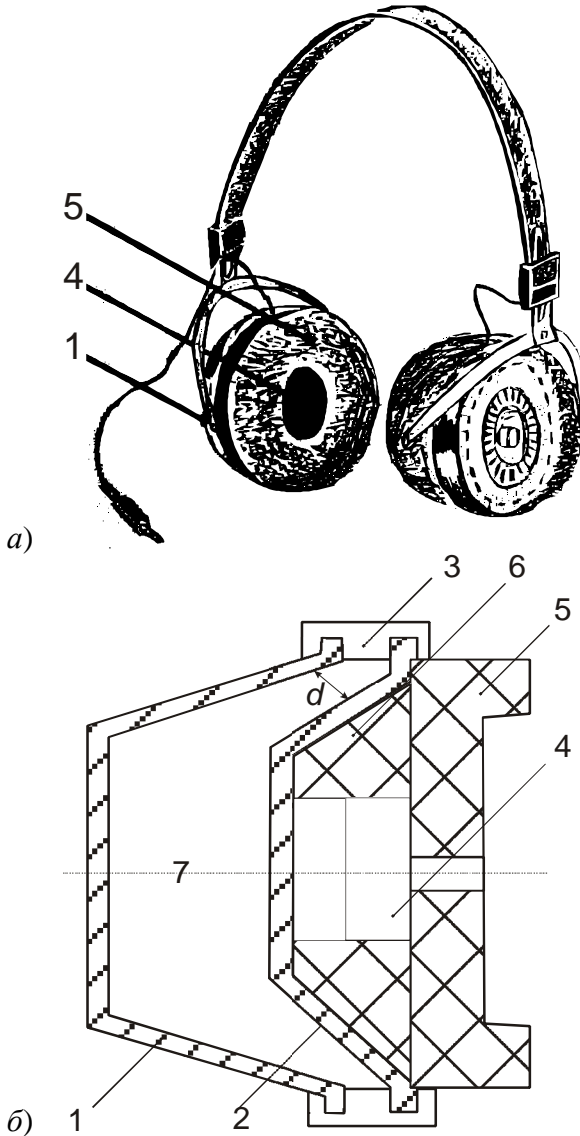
Головний телефон Абракітова [182]: *a* - зовнішній вигляд (дизайн) стереотелефонів; *б* - переріз: 1 - зовнішній корпус чашеобразної форми; 2 - внутрішній корпус чашеобразної форми; 3 - пружна прокладка, що герметизує; 4 - випромінювач акустичного
